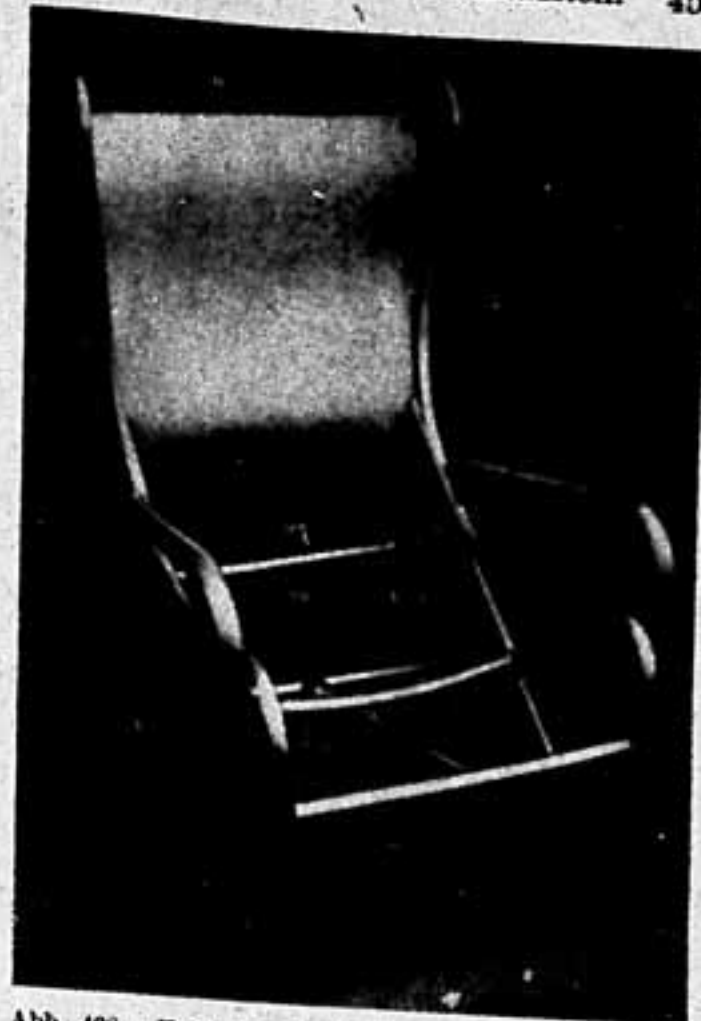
Kabinensessel für ein Verkehrsflugzeug in Elektronmetallrohren geschweißt.
